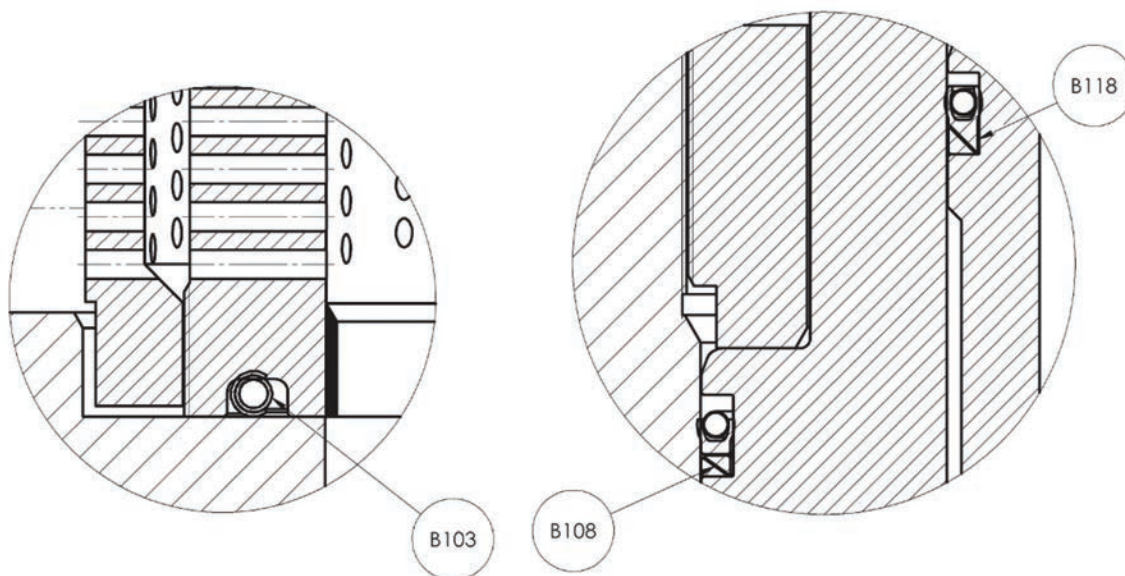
Монтаж уплотнений и прокладки для исполнения „поток на открытие“
